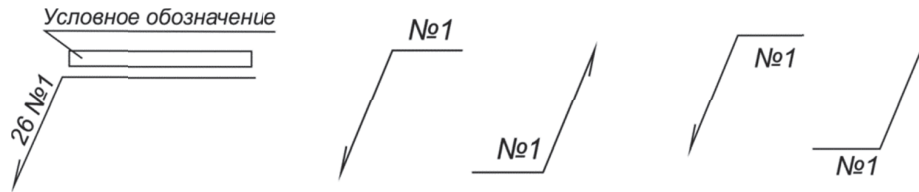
Условное обозначение сварного шва:
